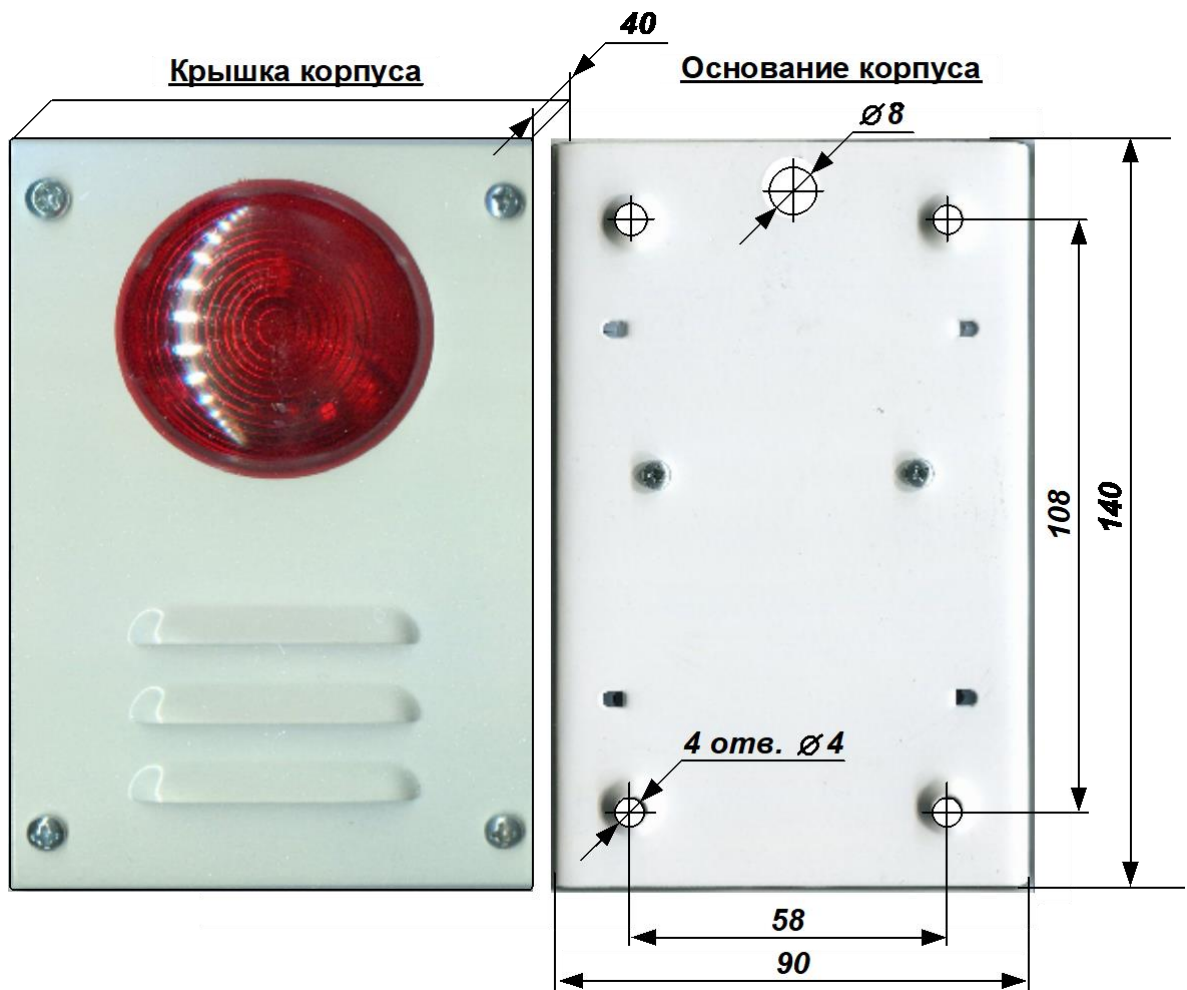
Внешний вид ОСЗ исп. 08 (габаритные и присоединительные размеры)
